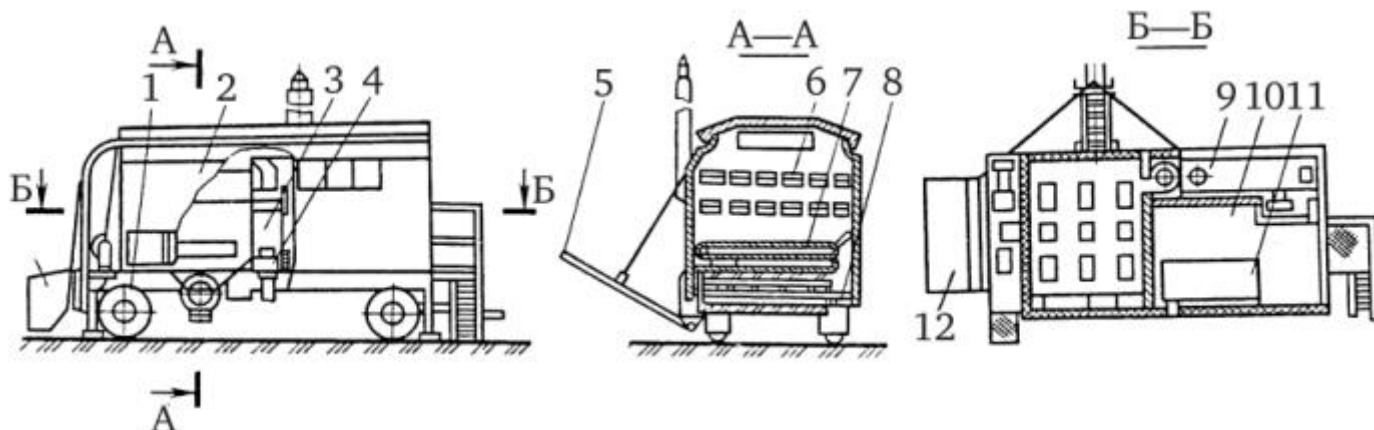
Передвижная шишкосушилка ШП-0,06:
